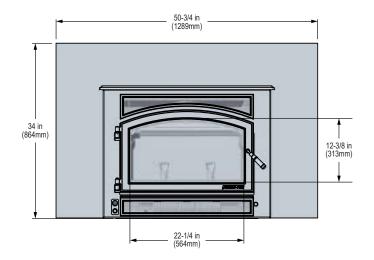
Vue frontale avec grand encadrement (SP2-5134)
